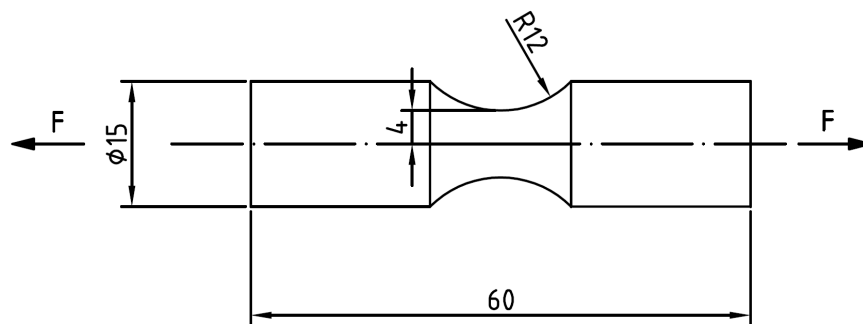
Geometria e direção de carregamento do provete axissimétrico com entalhe de raio 12 mm. Dimensões em mm.
